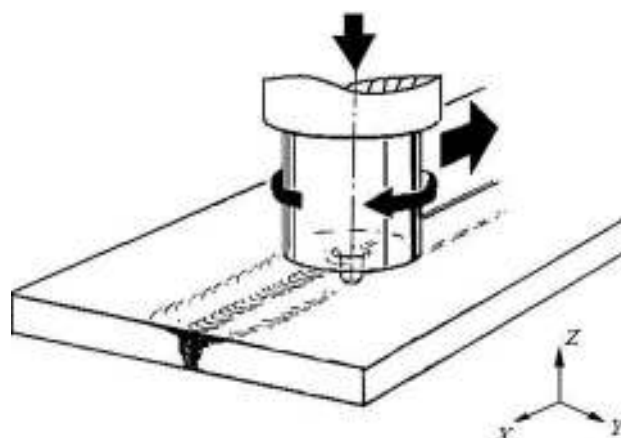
Схема процесса сварки трением с перемешиванием [17]
